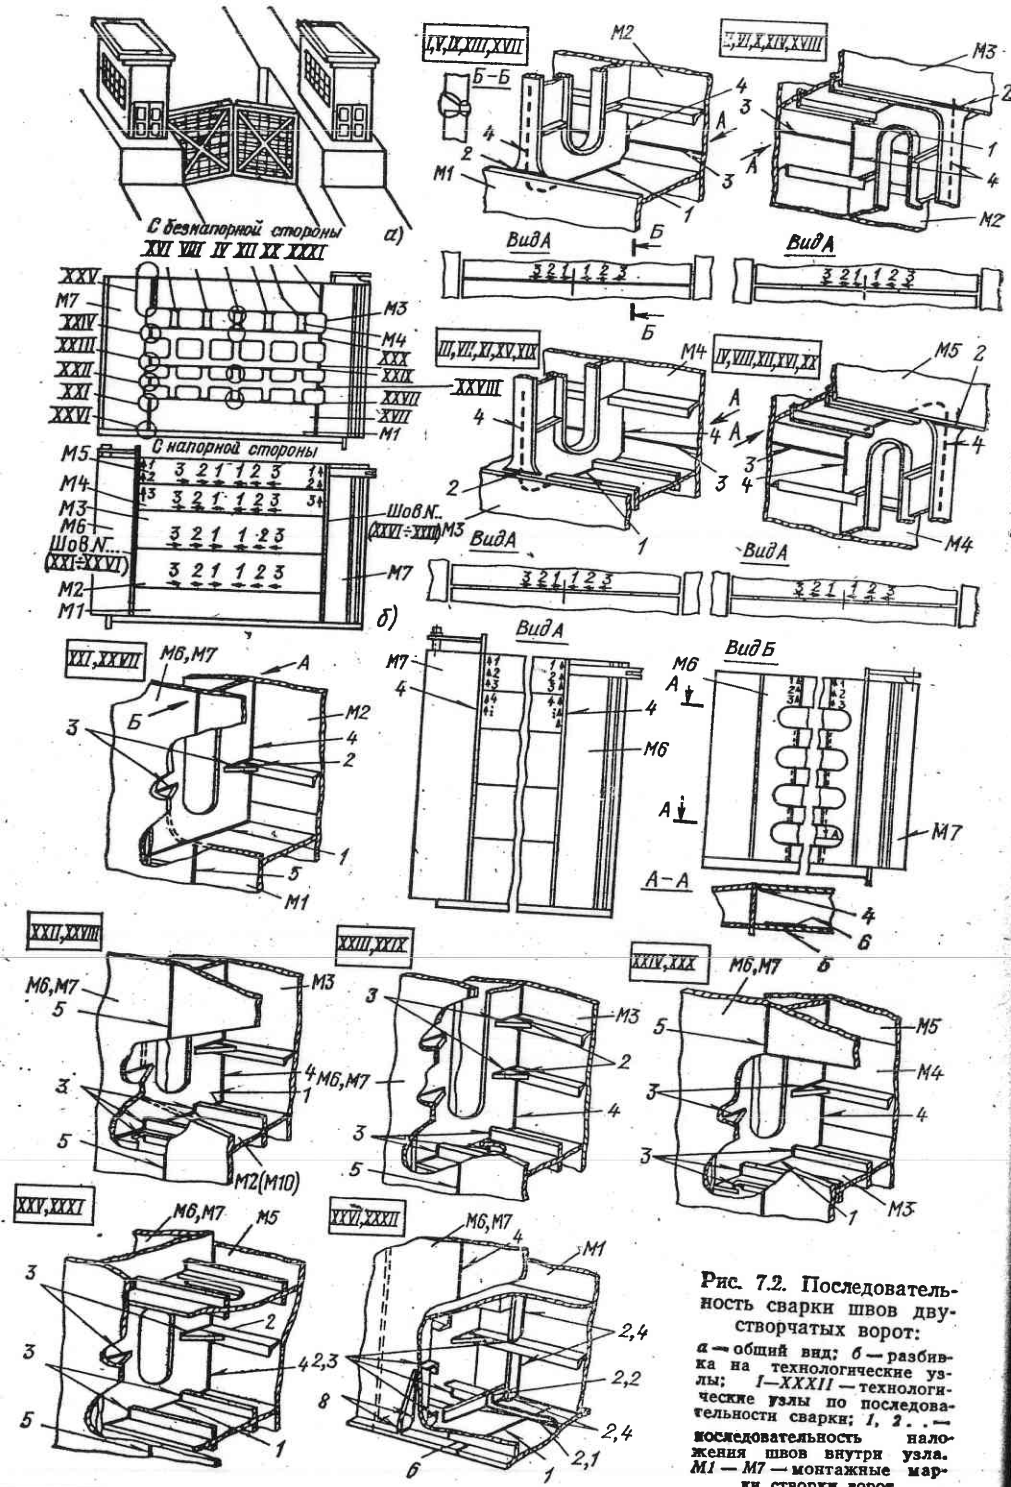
Последовательность сварки швов двустворчатых ворот:
